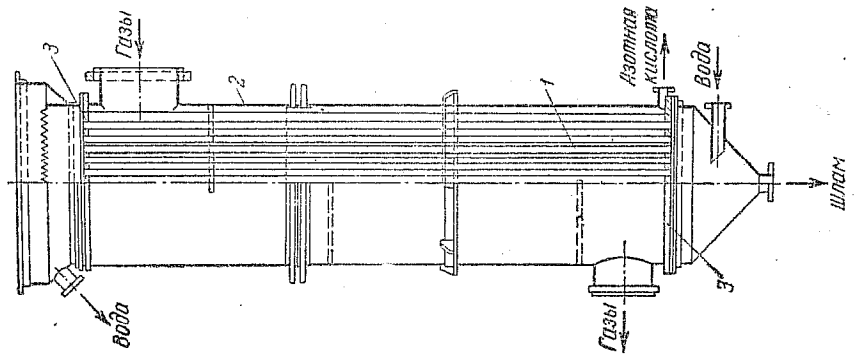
Газовый холодильник (поверхность охлаждения $290,5 \text{ м}^2$): 1—трубки; 2—корпус; 3—грубые решетки.
